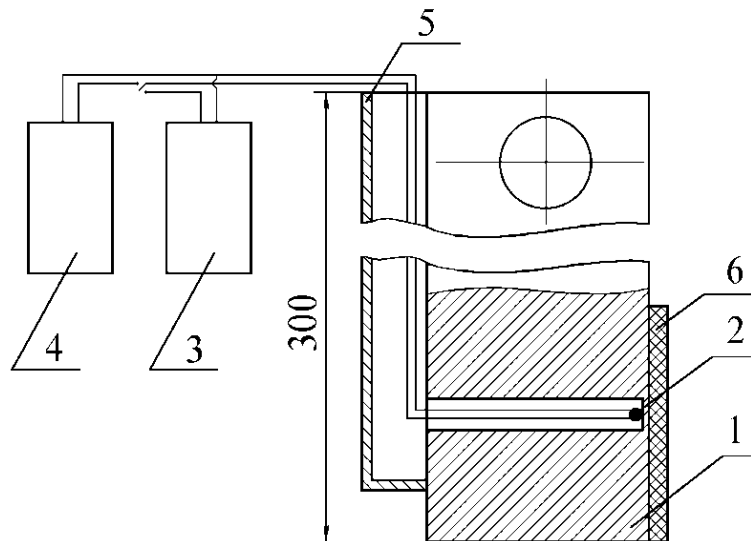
Схема измерения температуры наплавки: 1 – образец; 2 – термопара; 3 – шлейфовый осциллограф; 4 – вольтметр; 5 – защитный экран; 6 – наплавляемый слой
